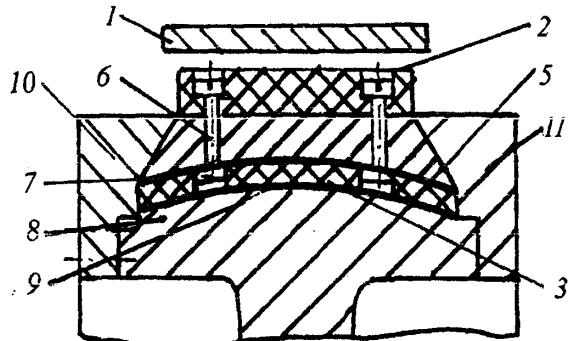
Схема стрічково-колодкового гальма з накладками посадженими з натягом на робочу поверхню гальмівного шківа
